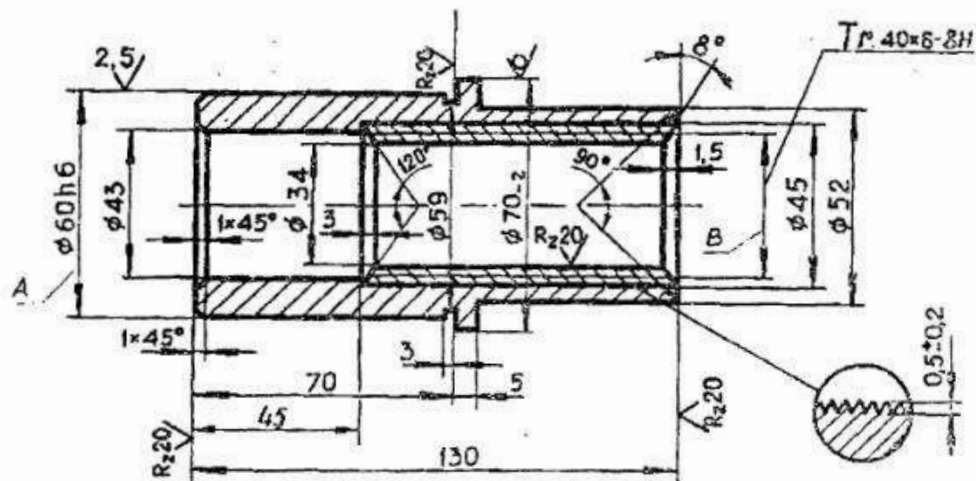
Гайка биметаллическая. Деталь 6P13.6.21A
